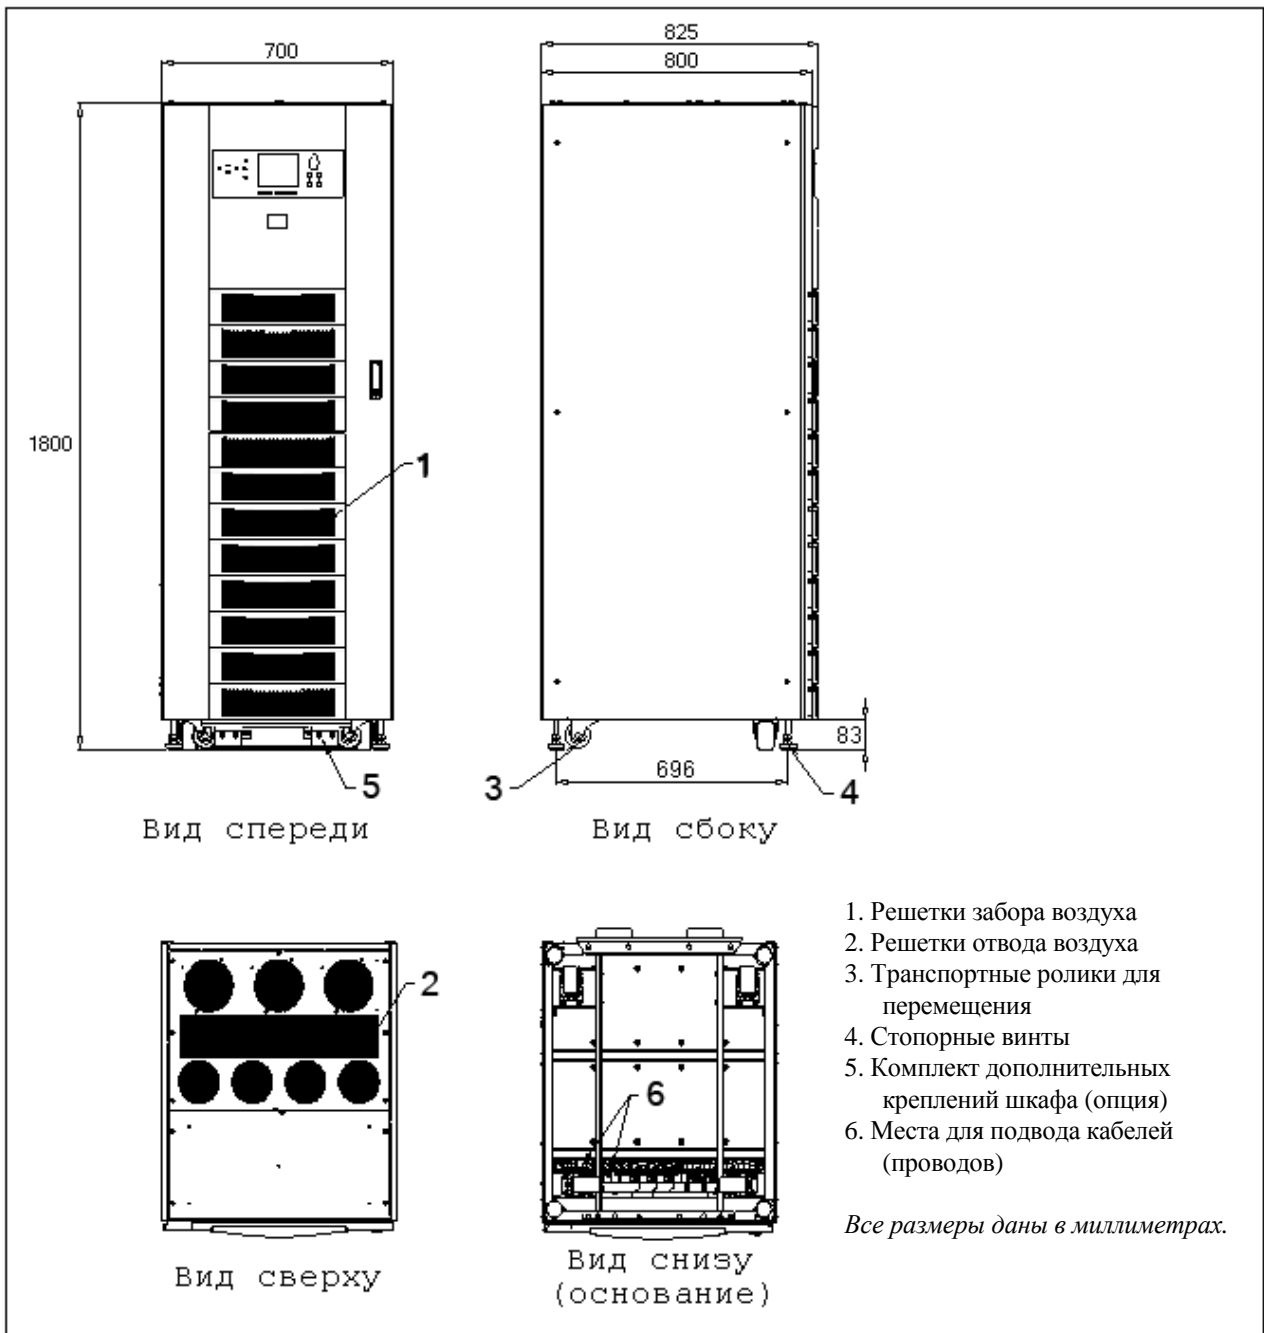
ИБП NXa 100-120 кВА, внешний вид и основные размеры
